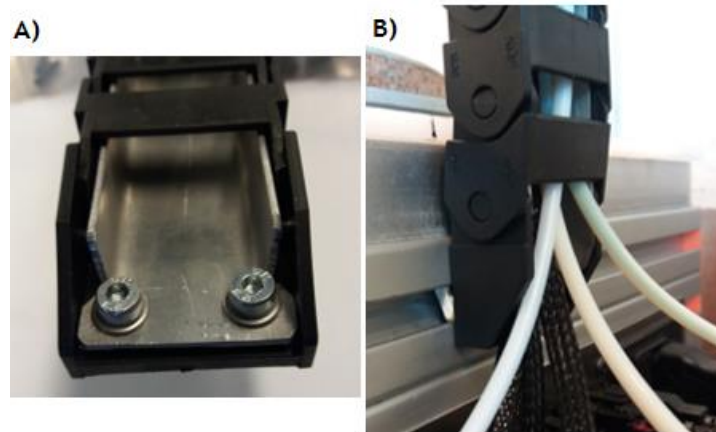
Modo de fixação através da chapa quinada de alumínio. A) vista frontal; B) vista lateral da fixação da guia ao perfil extrudido da base inferior da impressora.
